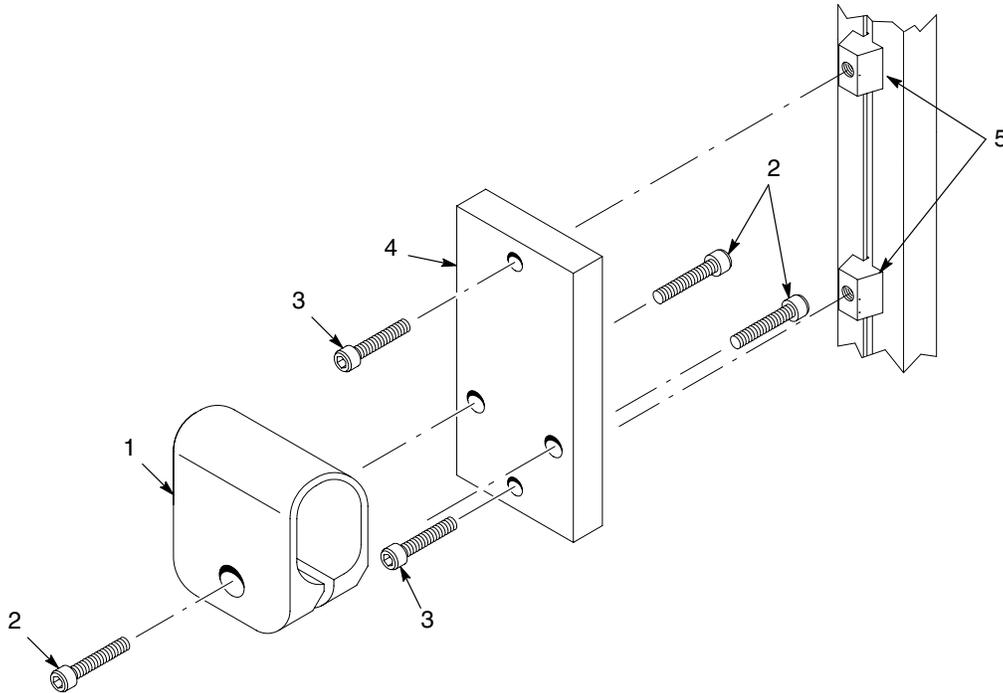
Conjunto de montaje de pistola de extrusión para pistolas de montaje en tubo
